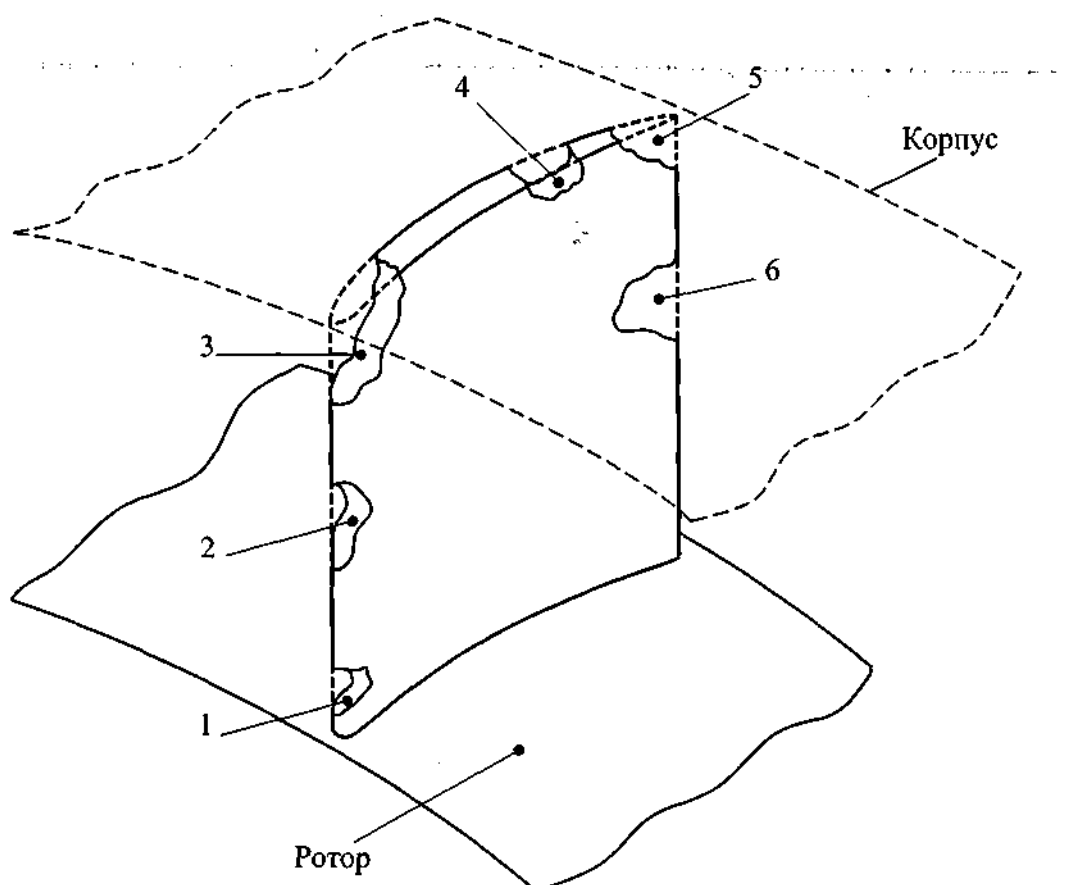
Основные виды повреждений лопаток компрессоров двигателей семейства Д-30:
